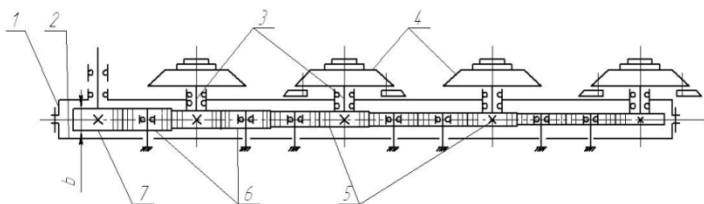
Роторный режущий аппарат с последовательно уменьшающейся шириной зуба шестерни: 1 – основной брус; 2 – крышка; 3 – валы; 4 – роторы; 5 – распределительные шестерни; 6 – промежуточные шестерни; 7 – приводная распределительная шестерня
